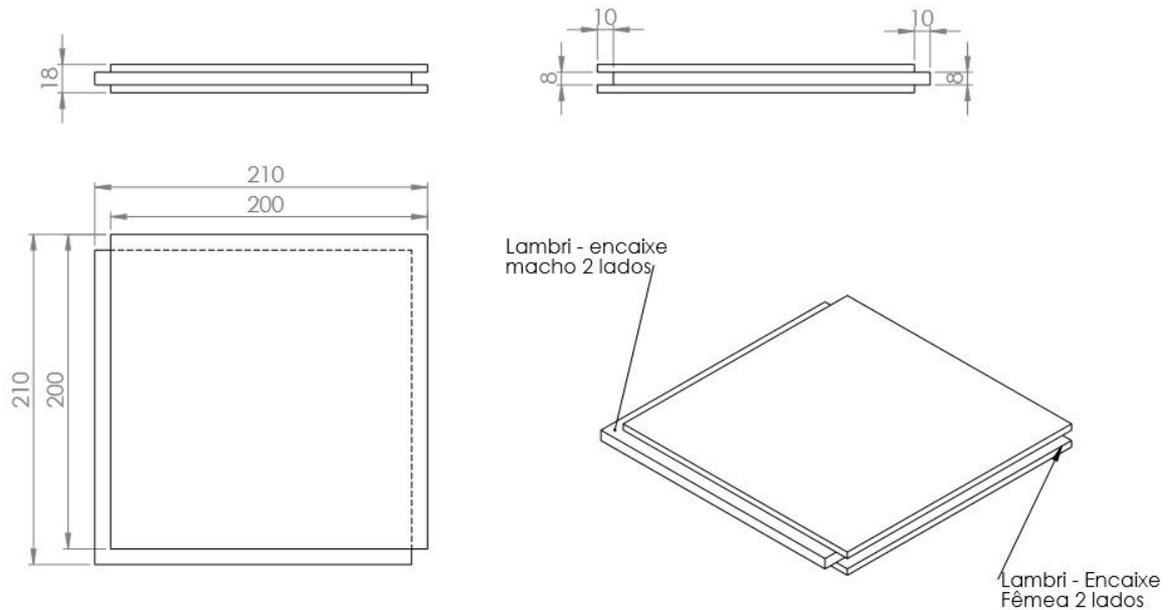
Desenho técnico dos módulos, com especificações em mm. Fonte: elaborado pelas autoras.
